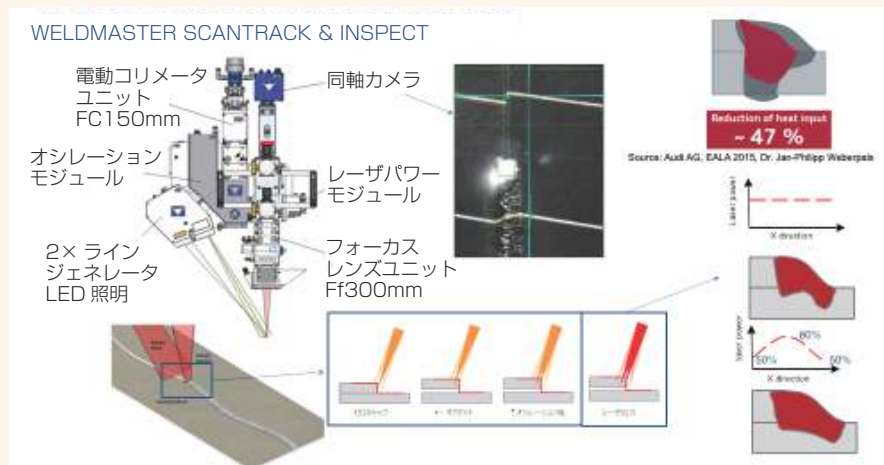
WeldMaster ScanTrack & Inspect。左がモニタリングヘッド。図の下方は、ワークにギャップがある場合の加工最適化プロセス。コリメータレンズにより溶接レーザビームに焦点位置を合わせる。ガルバノミラーを利用して、シームに対してレーザを垂直方向に振る。レーザを振ると、折り返し点でレーザ強度が高くなるため、レーザ出力を調整する。右端は、入熱量を47%削減したというAudiの報告。(提供:プレシテック社)
